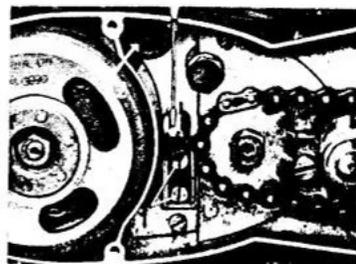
1 = Befestigungsschrauben des Lagerbockes
